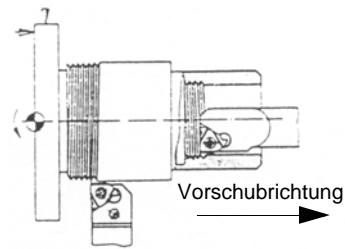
Linksgewinde bei Rechtslauf der Maschinenspindel
